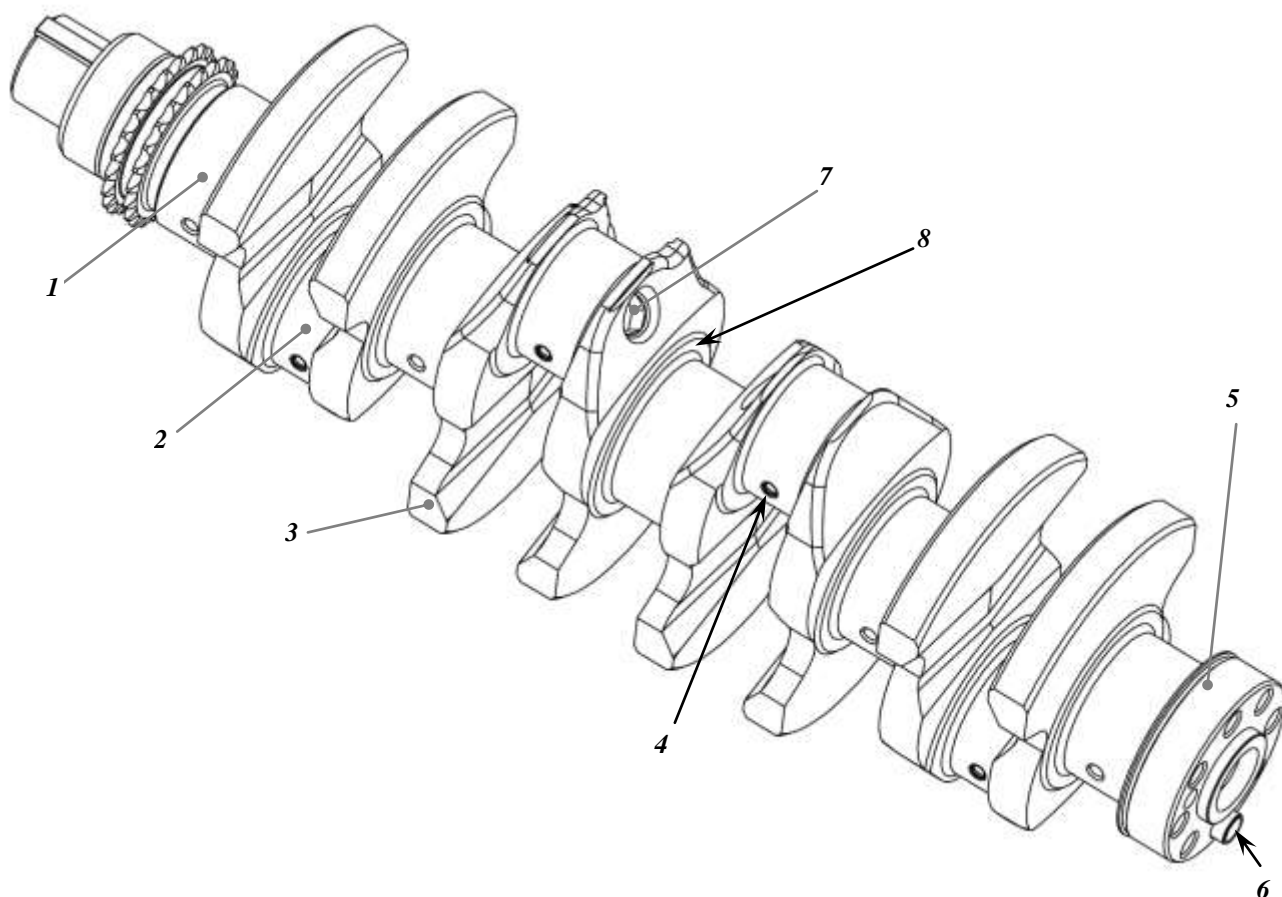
Вал коленчатый в сборе с пробками, установочным штифтом и звездочкой: 1 – 1-я коренная шейка; 2 – 1-я шатунная шейка; 3 – 3-й противовес; 4 – отверстие для подвода масла к 3-му шатунному подшипнику; 5 – шейка под задний сальник; 6 – втулка установочная маховика; 7 – пробка (заглушка) масляного канала; 8 – опорная поверхность под упорный подшипник.
